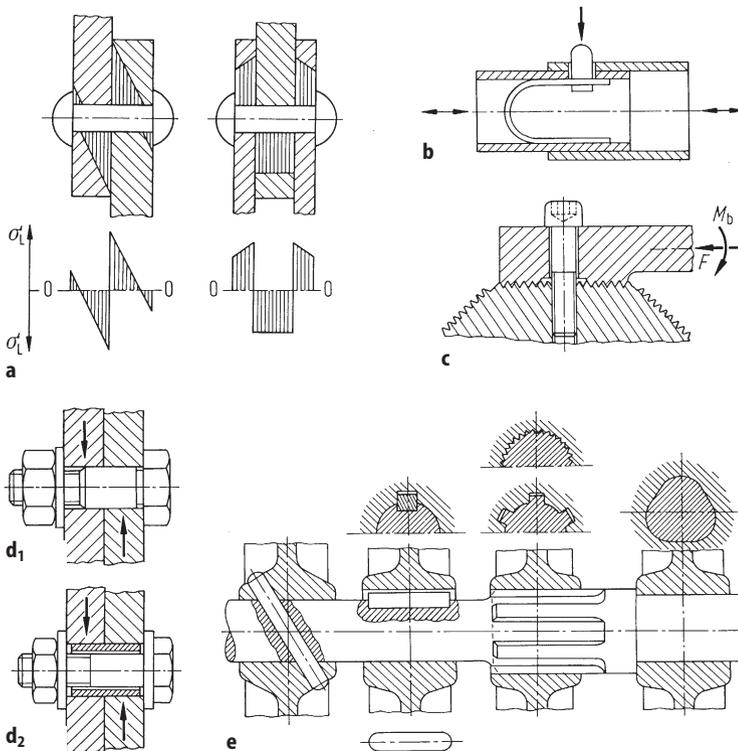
Bauformen von Formschlussverbindungen (Auswahl). a Ein- und zweischnittige Nietung (Lösbarkeit nur erschwert möglich); b Schnappverbindung; c vorgespannte Kerbverzahnung; d₁ querbeanspruchte Schraubenverbindungen mit Passschraube; d₂ mit Scherbuchse; e Welle-Nabe-Formschlussverbindungen
